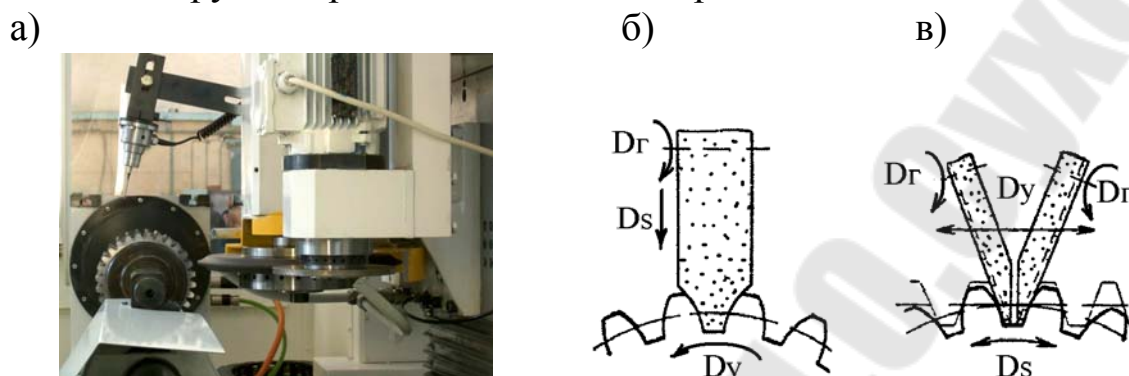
Рабочая зона зубошлифовального станка (а) и схемы шлифования зубчатых колес (б, в)
